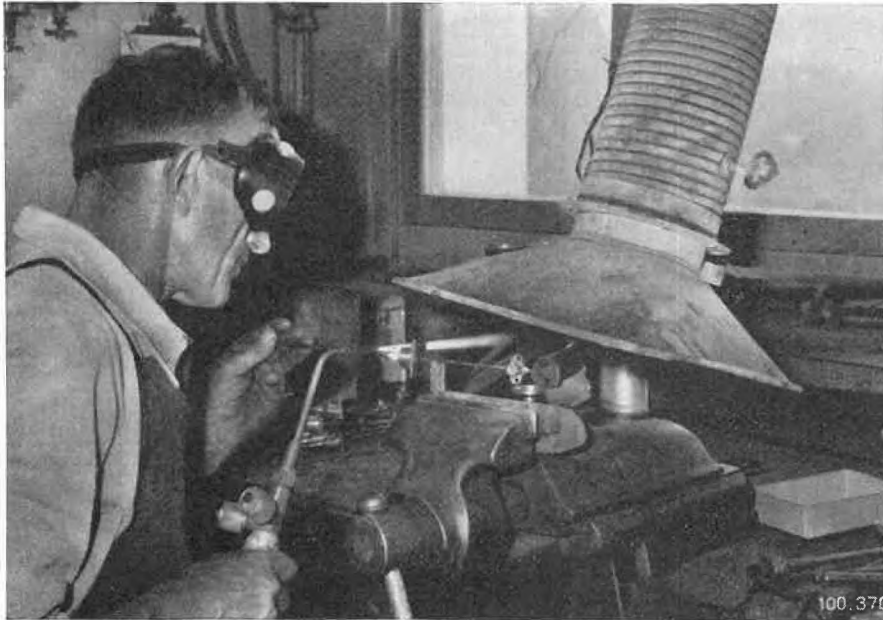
Absaugeinrichtung beim Verschweißen von Thermometerfühlern
